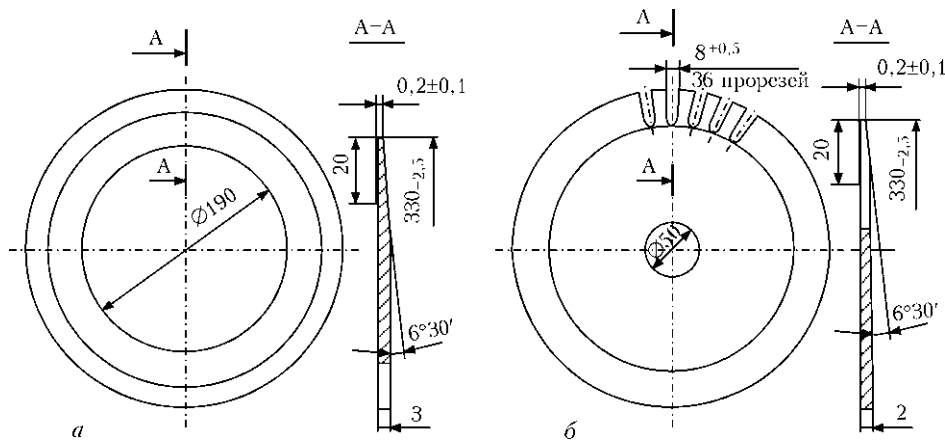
Схема конструкции дисковых ножей [12]: а — неприводной; б — приводной
